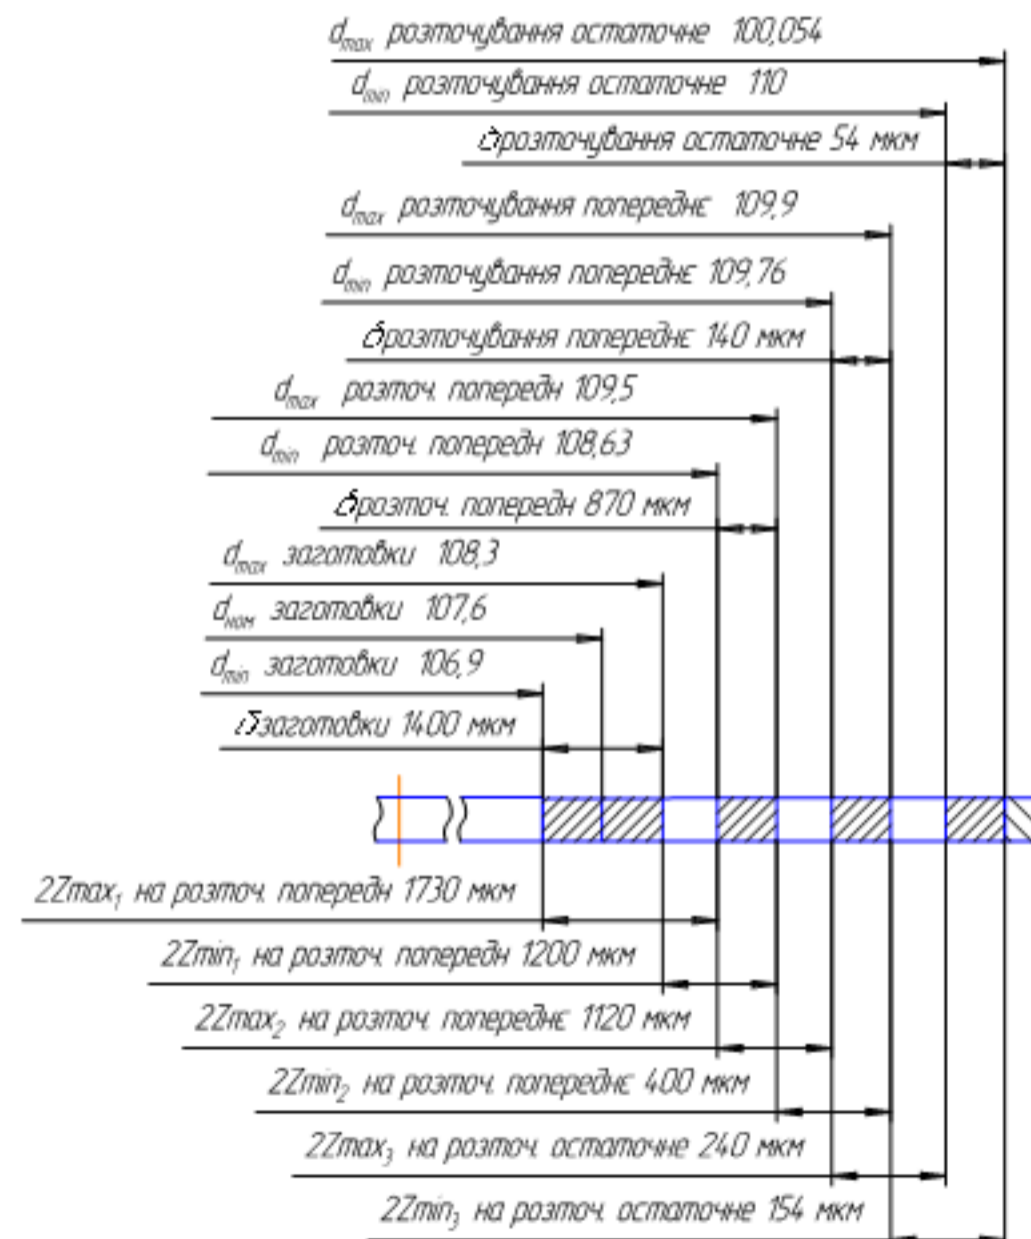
Схема графічного розташування припусків і допусків на обробку
